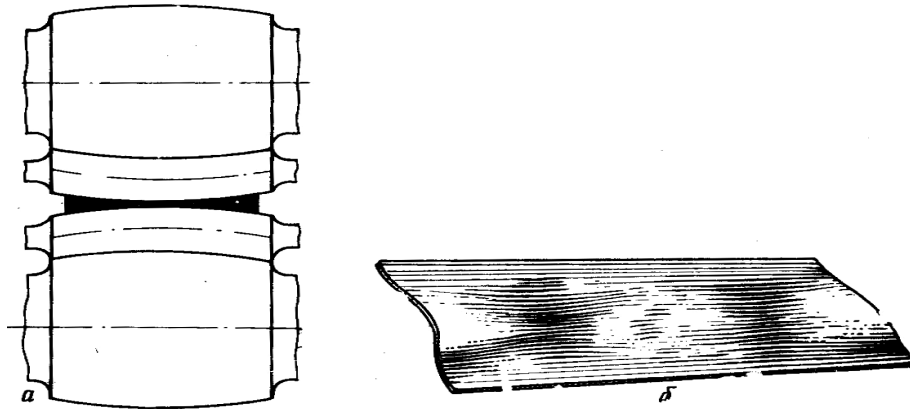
Вплив надмірної опуклості бочки валка на якість і поверхню штаби
